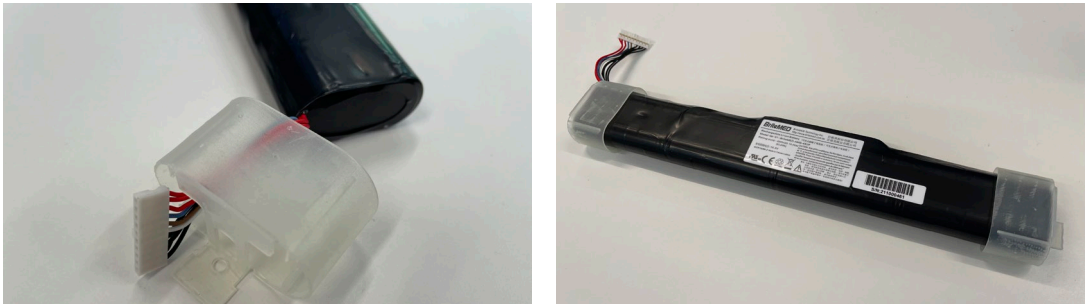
Montaje de las tapas de la batería como muestran las flechas
